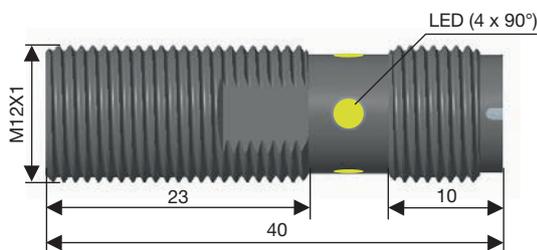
Kurze Ausführung, bündiger Einbau, Steckversion
